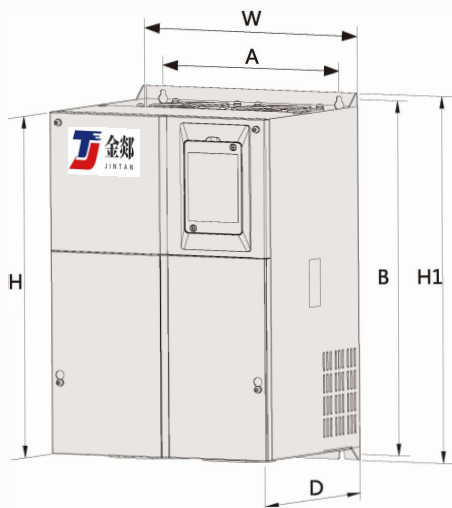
JT960 系列 钣金结构外型尺寸及安装尺寸示意图
